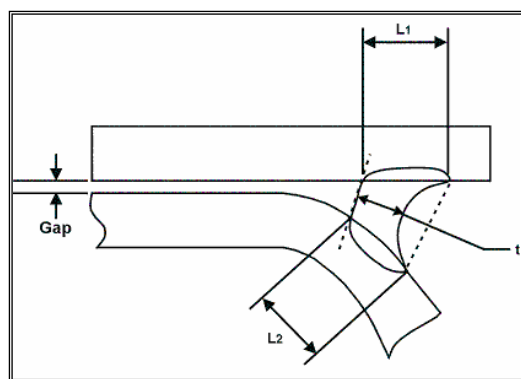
Soldadura de ranura en chasis , ranura flare ^[1]
